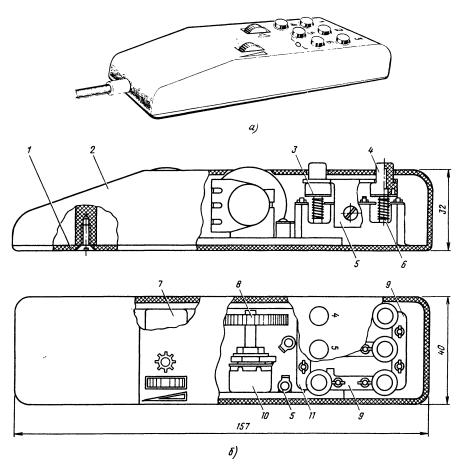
Конструкция пульта ДУ «Радуга»: a — внешний вид; δ — разрез (I — основание; 2 — корпус; 3 — контактная шайба; 4 — кнопка; 5 — держатель; 6 — пружина; 7 — переменный резистор яркости; δ — ручка громкости; 9, 11 — контактная пластина; 10 — переменный резистор регулировки громкости)
